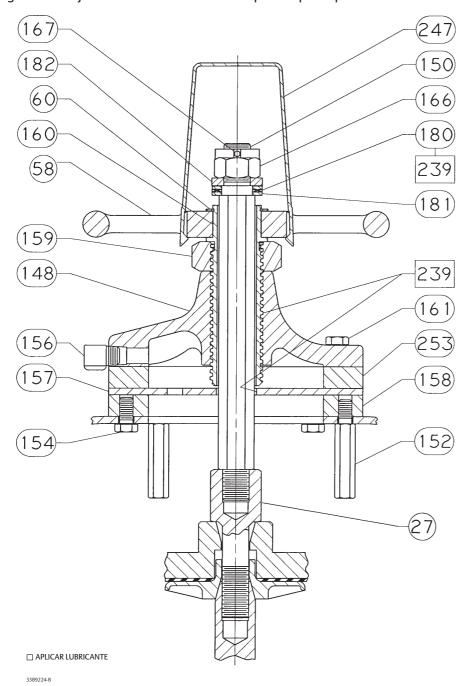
Conjunto de volante montado en la parte superior para actuadores tamaños 70 y 87
